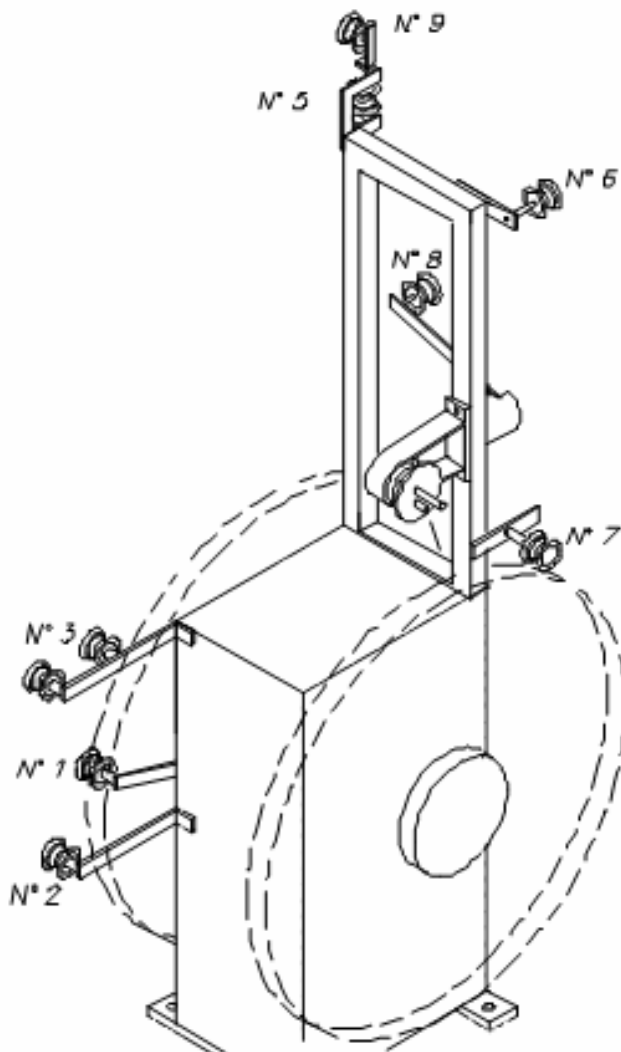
сборка роликов и рычагов на стойке PL 5000
